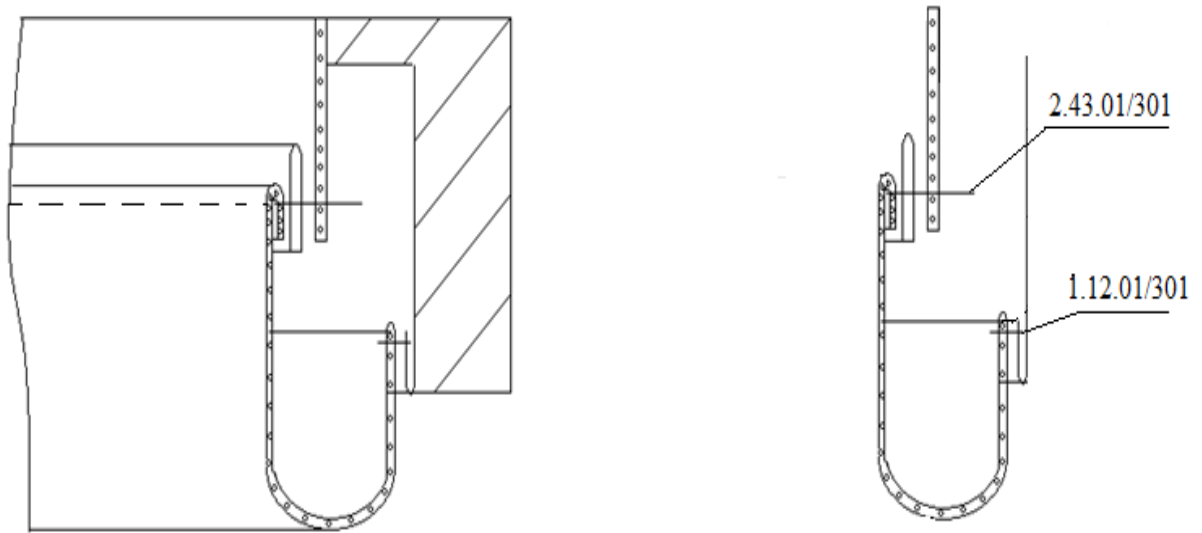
Обробка манжети та з'єднання її з рукавом
